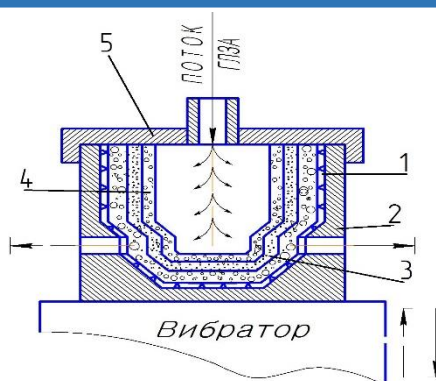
Контейнер для изготовления. 1-спекания пористая заготовка; 2-корпус контейнера; 3-слой мелкого порошка; 4- проницаемый элемент; 5- крышка.
